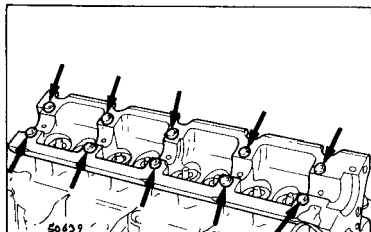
Проверьте, чтобы установочные втулки крышек подшипников распредвала были на месте
